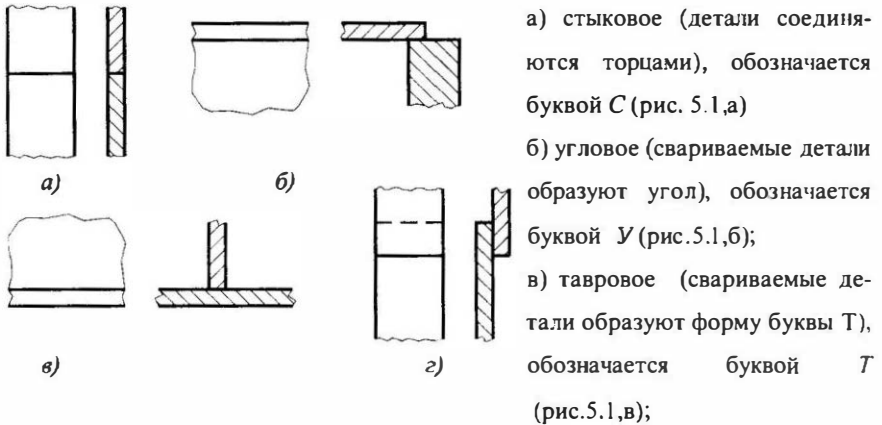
Типы сварных соединений: а) – стыковое; б) – угловое; в) – тавровое; г) – внахлестку
